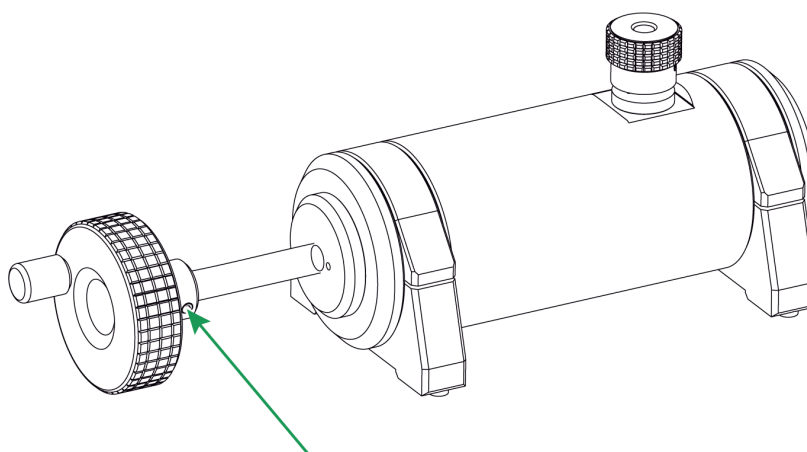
Remontage du sous-ensemble de réglage grossier
